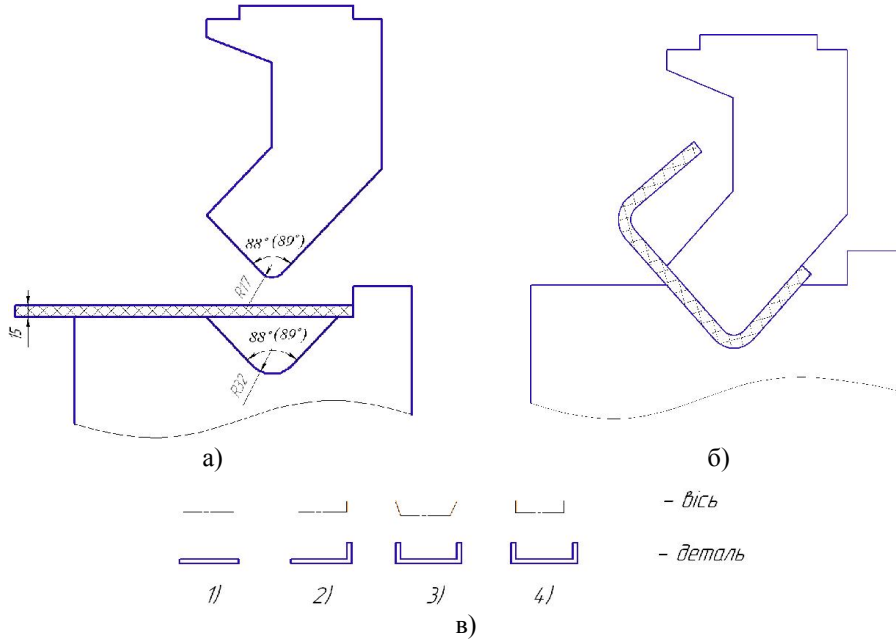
Поелементне гнуття деталі інструментом із плоскими контактними поверхнями:
